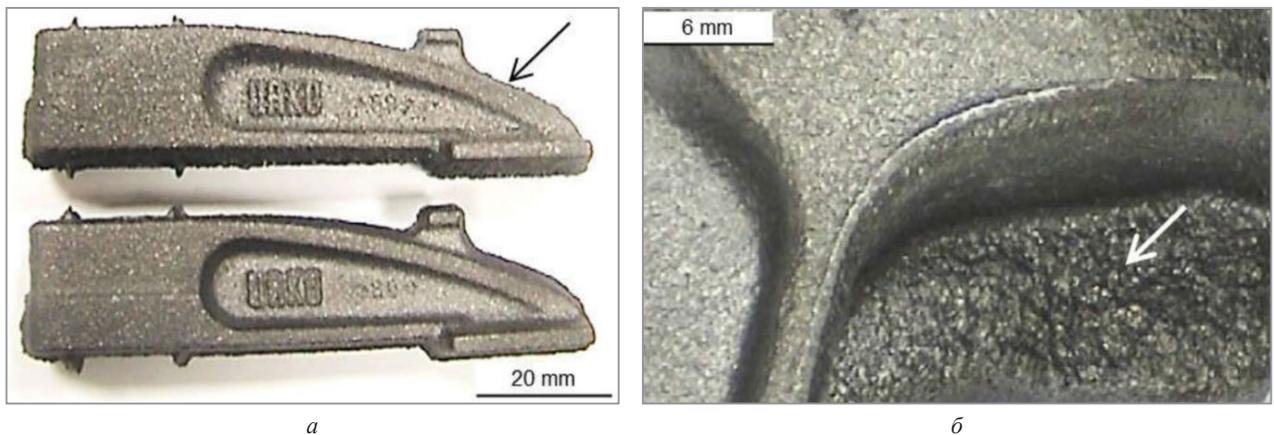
Дефекты отливки «Грубая шероховатость»
